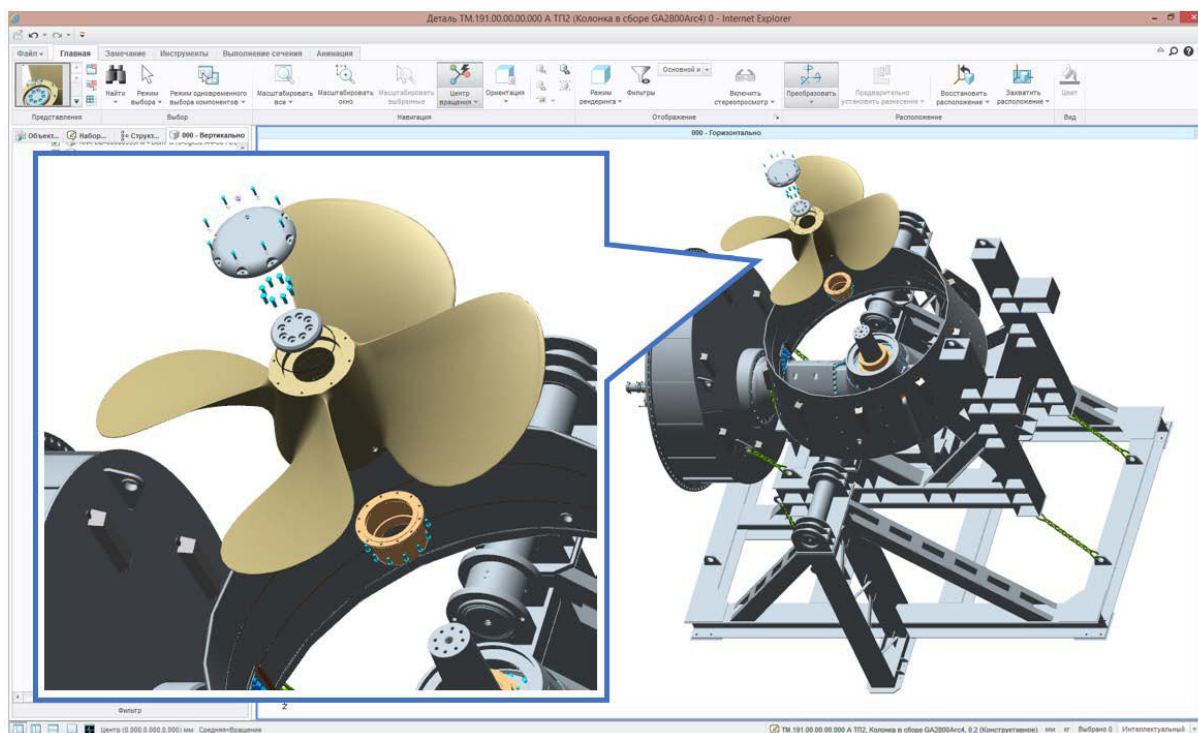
ИЭТР для сборки винторулевой колонки в CAD-системе
